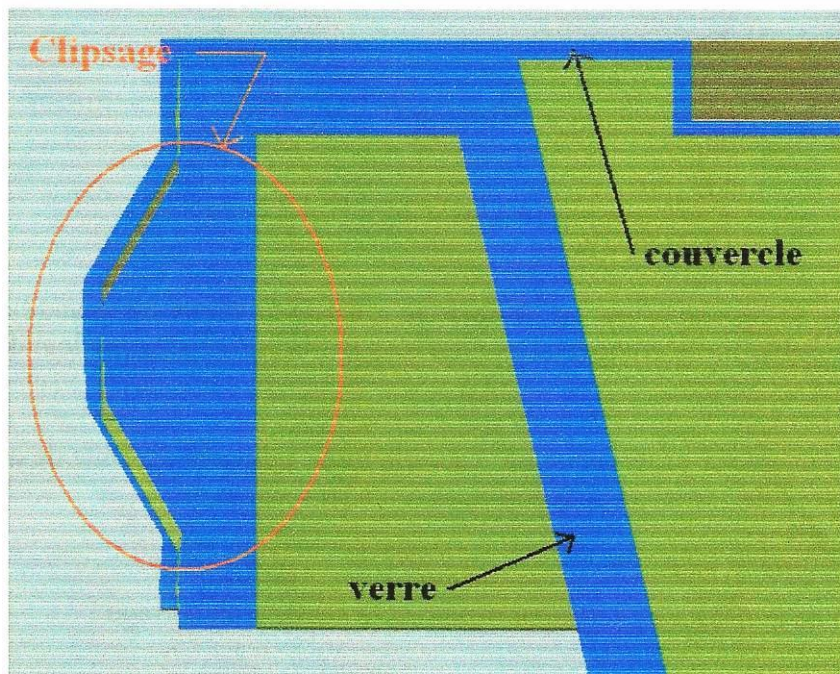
Vue d'une coupe en section de l'assemblage par clipsage du verre/couvercle
